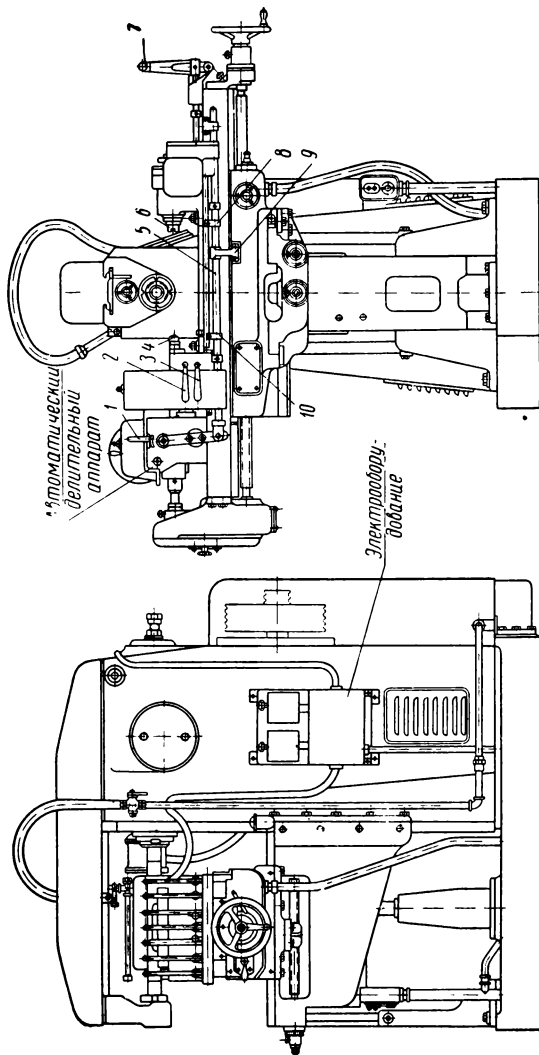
Полуавтомат мод. 6С209 для фрезерования канавок в метчиках:
